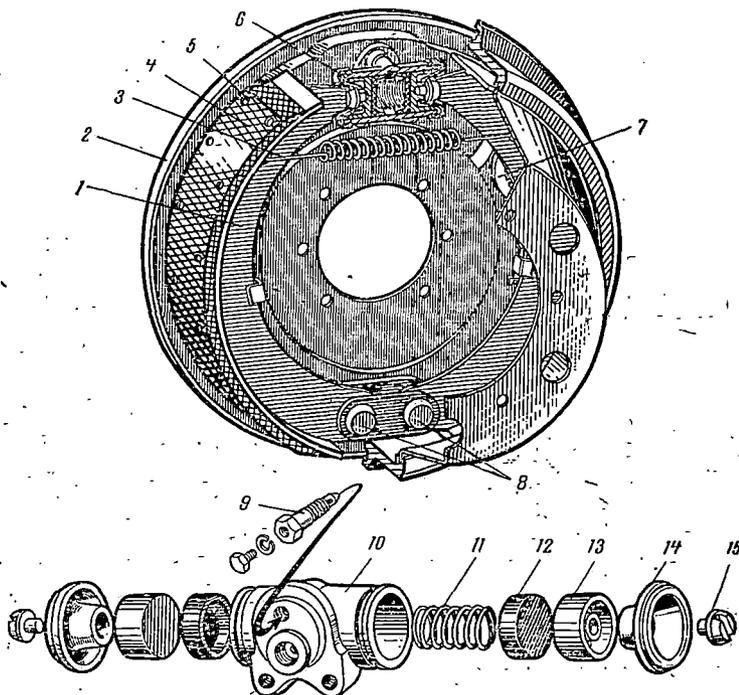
Схема колесного тормоза автомобиля ГАЗ-51А:
